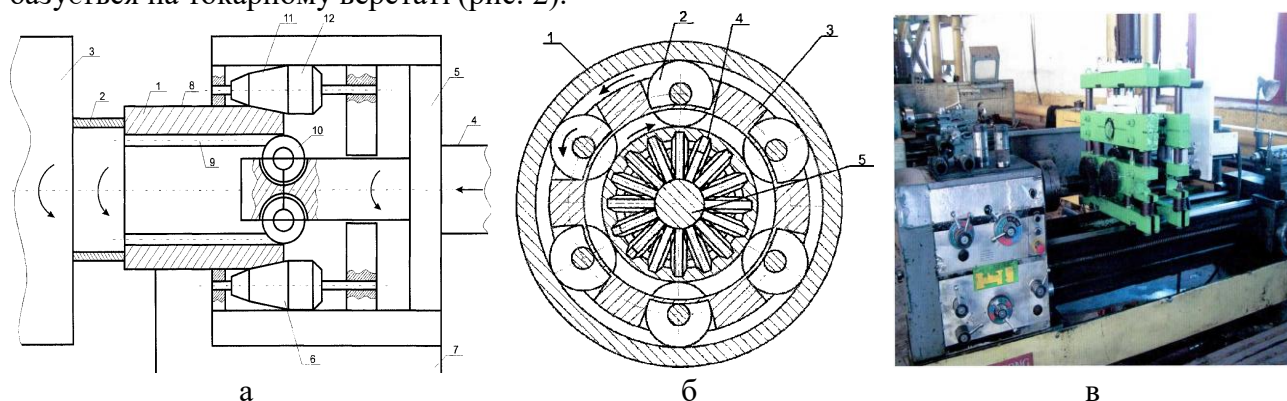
Пристрій для відновлення шліцевих втулок: а) - загальна схема; б) - схема конструкції накатної оснастки; в) - компонування пристрою на токарно-гвинторізному верстаті 16К20
